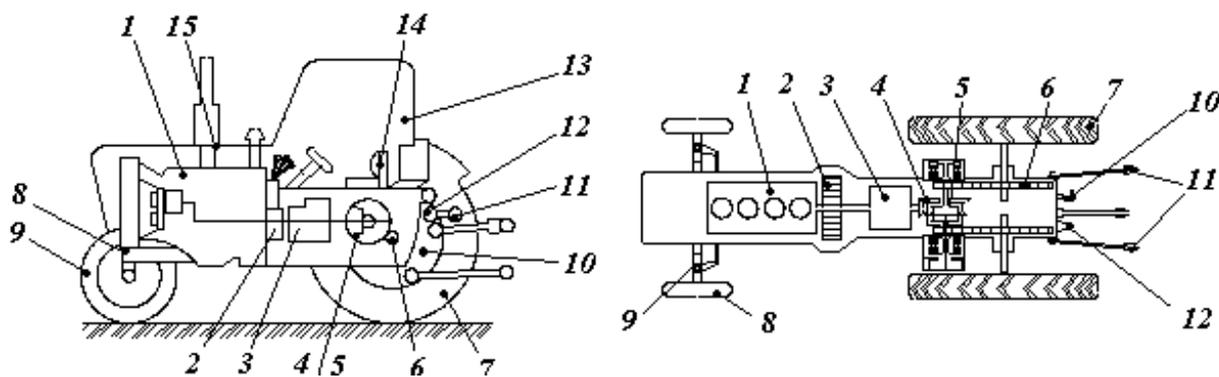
Расположение механизмов и сборочных единиц колесного трактора типа МТЗ:
